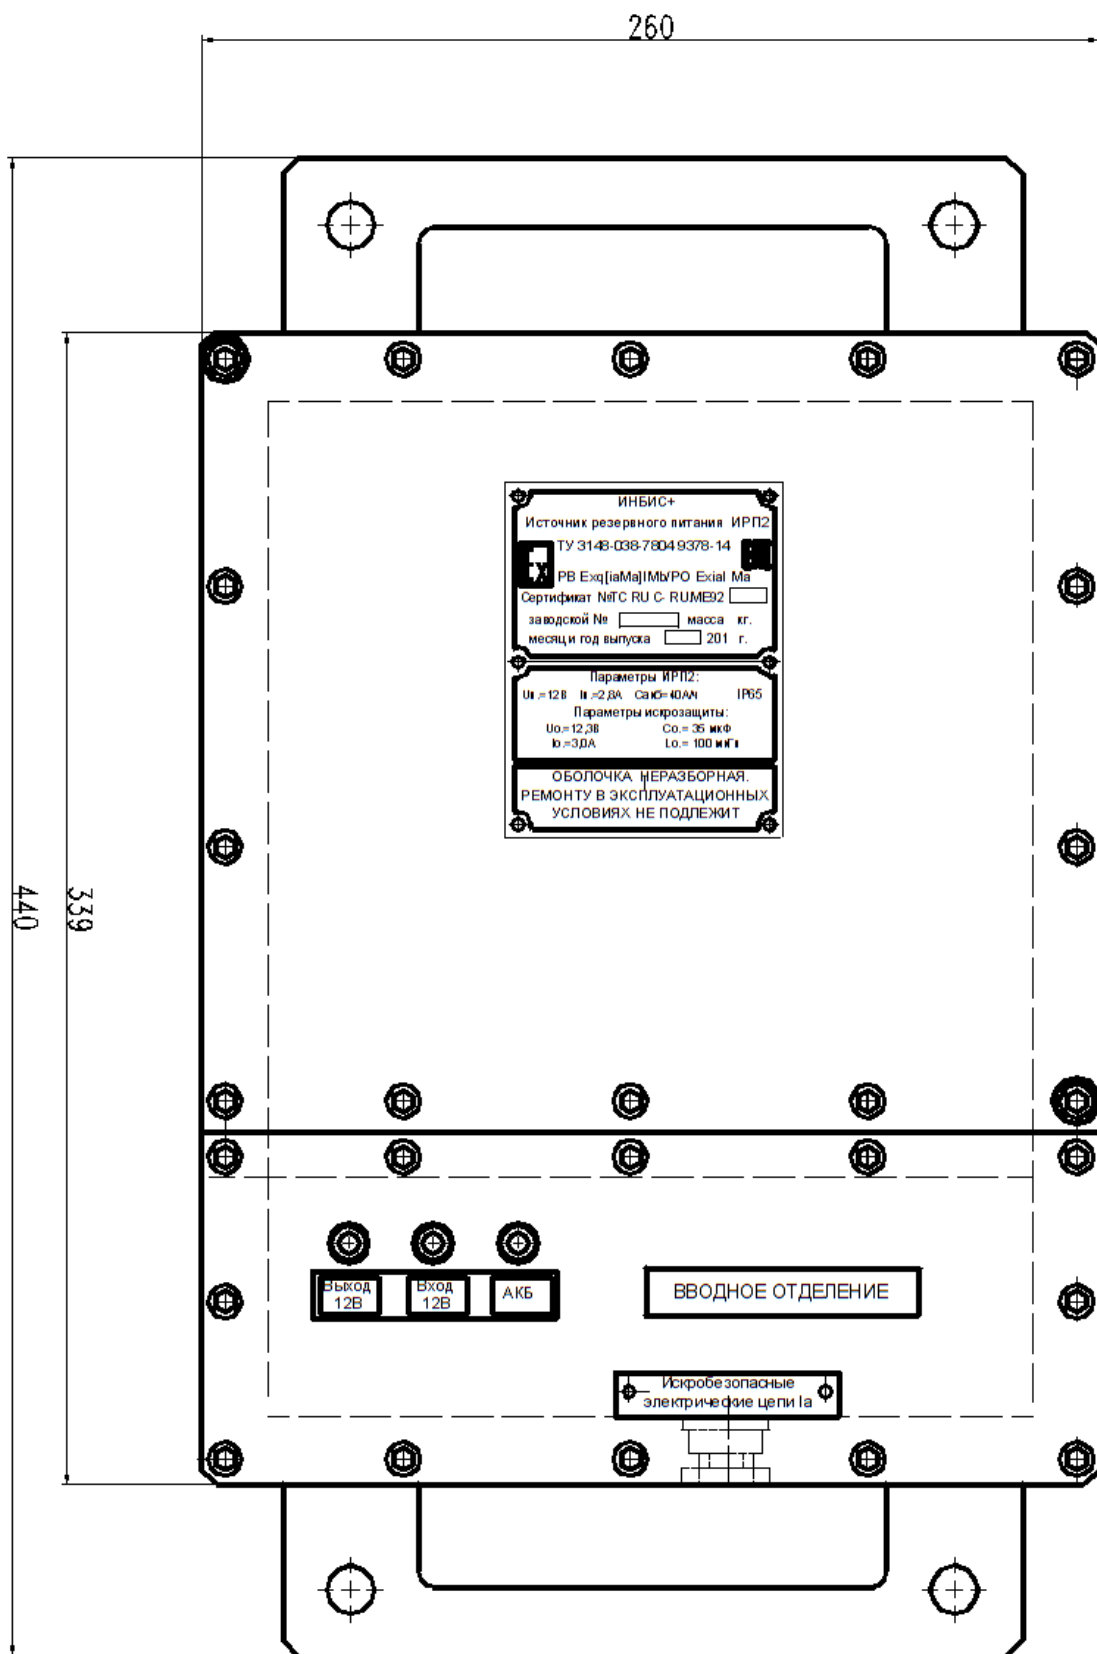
Общий вид и габаритные размеры источника резервного питания ИРП2
